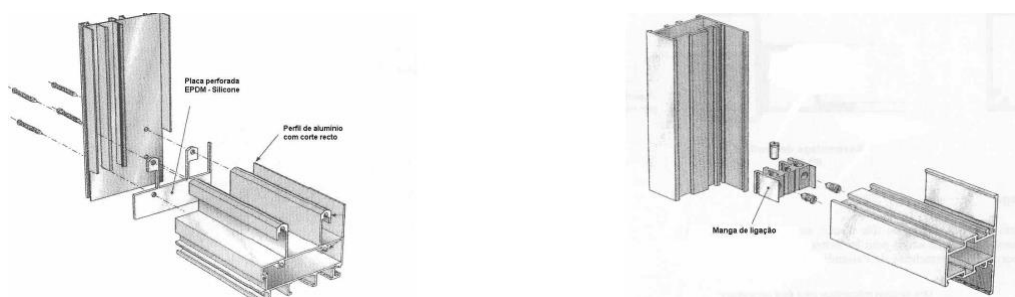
\_ Ligação em corte reto e em T ou cruz (Verdelho, 2005)
